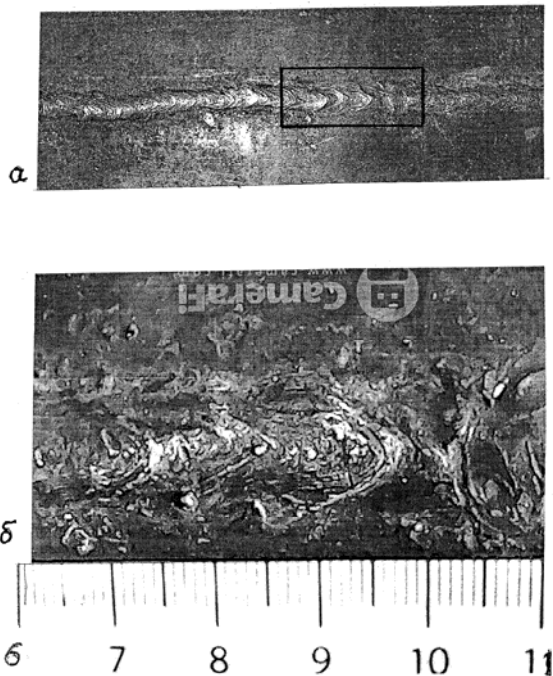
Образец сварного соединения (а) и его фрагмент (б) зоны возможного расположения внутренних дефектов с тремя поверхностными парами
